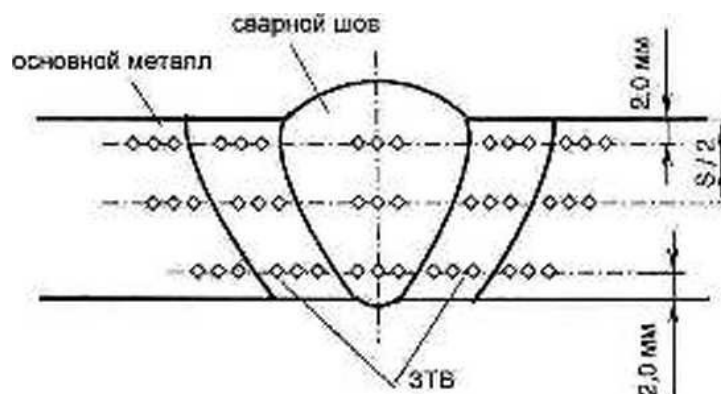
Схема измерения твердости (HV10) в различных зонах сварного соединения
